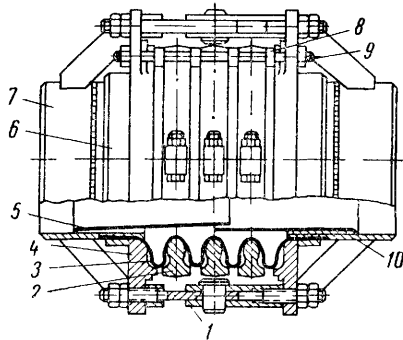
Компенсатор волнистый универсальный шарнирного типа
